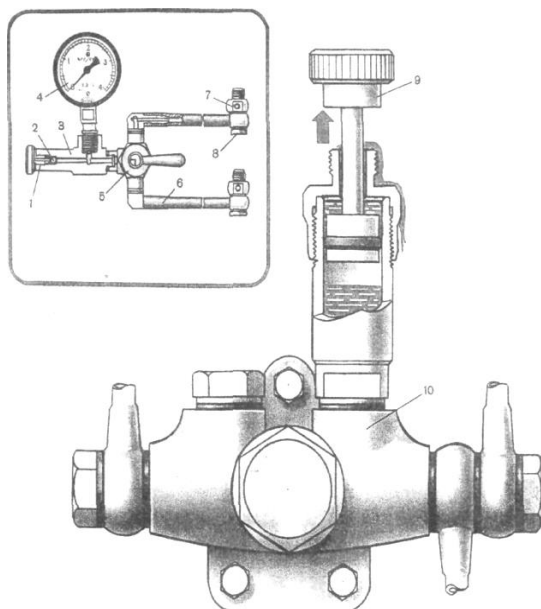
Пристрій КИ-4801 і паливopідкачувальний насос дизеля: 1 – гвинт клапану; 2 – шариковий клапан для випуску повітря; 3 – корпус пристрою; 4 – манометр; 5 – двоходовий кран; 6 – гнучкий паливopровід; 7 – поворотний кутник; 8 – болт поворотного кутника; 9 – ручний насос; 10 – паливopідкачувальний насос.
